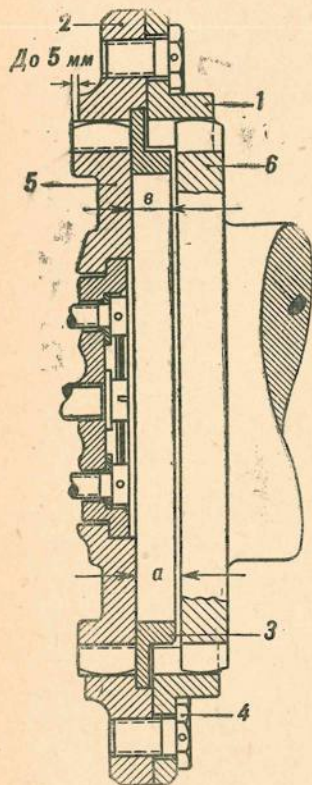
Муфта полужесткого соединения коробки перемены передач
